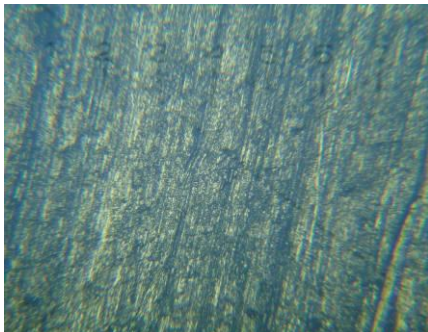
Шероховатость обработанной поверхности после торцевого фрезерования
